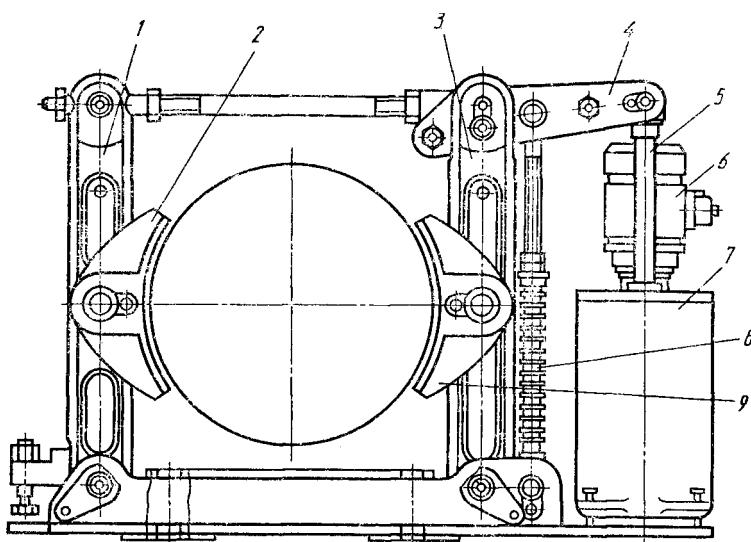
Колодочный пружинный тормоз с электрогидротолкателем
